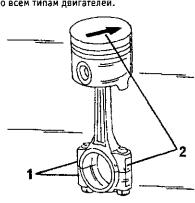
Правильная сборка поршня и шатуна. Метки на шатуне и крышке подшипника (1), а также маркировка "DT" и вырез под вкладыши подшипника (2) должны быть ориентированы так, как показно на рисунке. Поршневые пальцы 16-клапанного двигателя крепятся стопорными кольцами.
